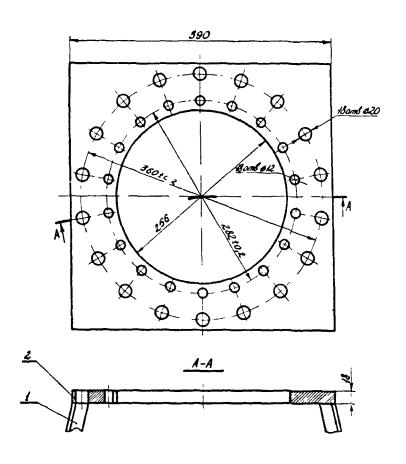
Подставка для разборки и сборки гасительной камеры и отделителя:
